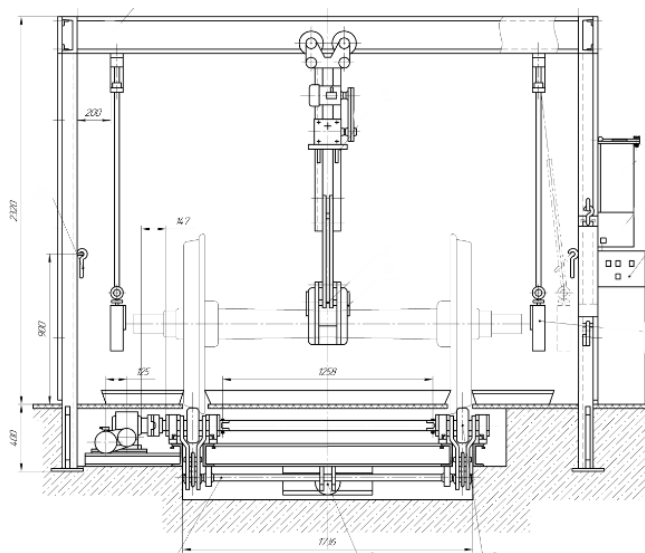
Стенд магнітопорошкового контролю осей колісних пар
